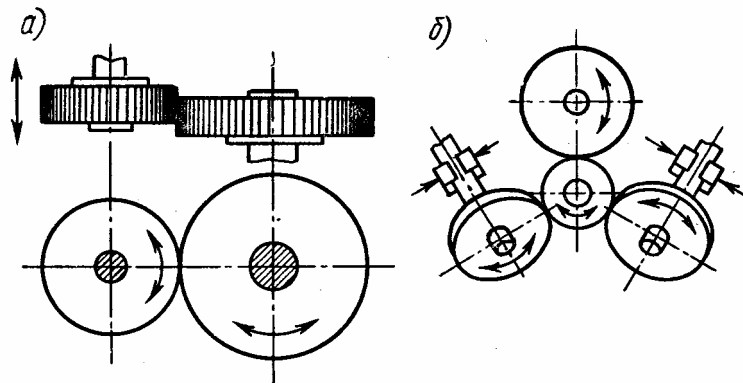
Схемы притирки зубьев цилиндрических зубчатых колес:
